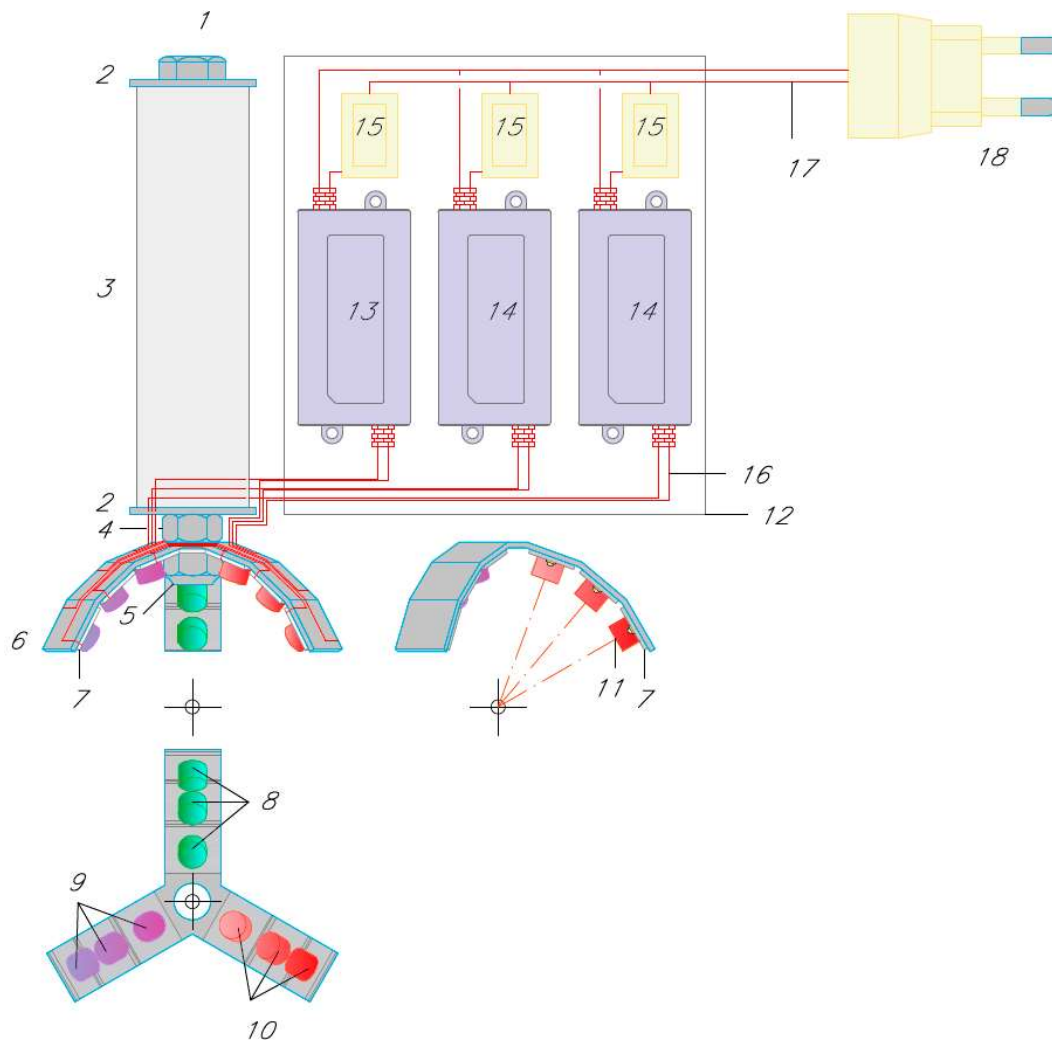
Diseño equipo. 1.-Tornillo ensamblaje cuerpo - pieza aluminio de triple brazo. 2.-Arandela cierre cuerpo. 3.-Brazo material plástico aislante. 4.-Tuerca posicionamiento pieza aluminio triple brazo. 5.-Tuerca autoblocante fijación ensamblaje. 6.-Pieza aluminio triple brazo disposición de matrices LED. 7.-Placa PCB para disposición de diodos LED alta potencia. 8.-Diodo LED alta potencia 522 nm. 9.-Diodo LED alta potencia 404 nm. 10.-Diodo LED alta potencia 632 nm. 11.-Lente concentradora 20°. 12.-Caja aislada disposición de drivers. 13.-Driver matriz LED 404 nm - 12W. 14.-Driver matriz LED 522 nm y 632 nm - 8W. 15.-Botonera encendido/apagado matriz LED. 16.-Cableado alimentación CC matriz LED. 17.-Cableado alimentación CA tensión monofásica red (230V - 50Hz). 18.-Clavija conexión red baja tensión.
